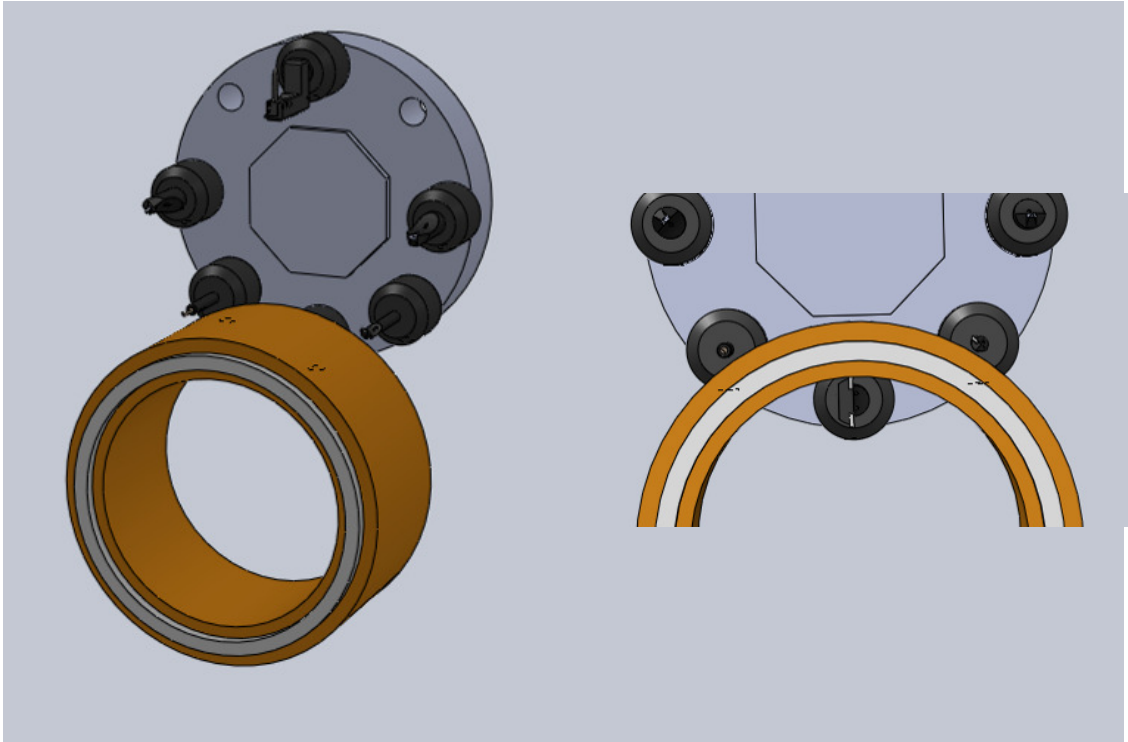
8-fach Werkzeugwender Durchmesser 300mm mit Halbzeug 265/350
